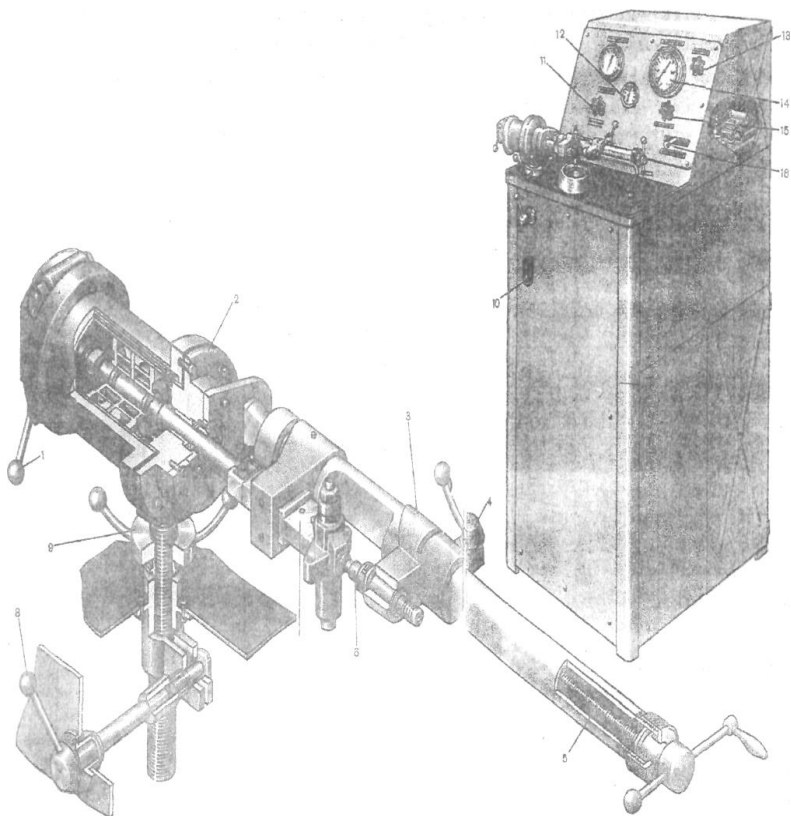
Стенд КИ-1404 для випробовування форсунок: 1 – двоходовий кран; 2 – пневматичний циліндр; 3 – установочний штуцер; 4 – фіксуєчий пристрій (стопор); 5 – установочний гвинт; 6 – штуцер паливопроводу високого тиску; 7 – натискна призма; 8 – стопор; 9 – підйомний гвинт; 10 – кнопки "Пуск" і "Стоп"; 11 – кран манометру низького тиску; 12 – секундомір; 13 – кран манометру високого тиску; 14 – манометр високого тиску; 15 – кран подачі палива до форсунки, що перевіряється; 16 – рукоятка збільшення подачі палива.
